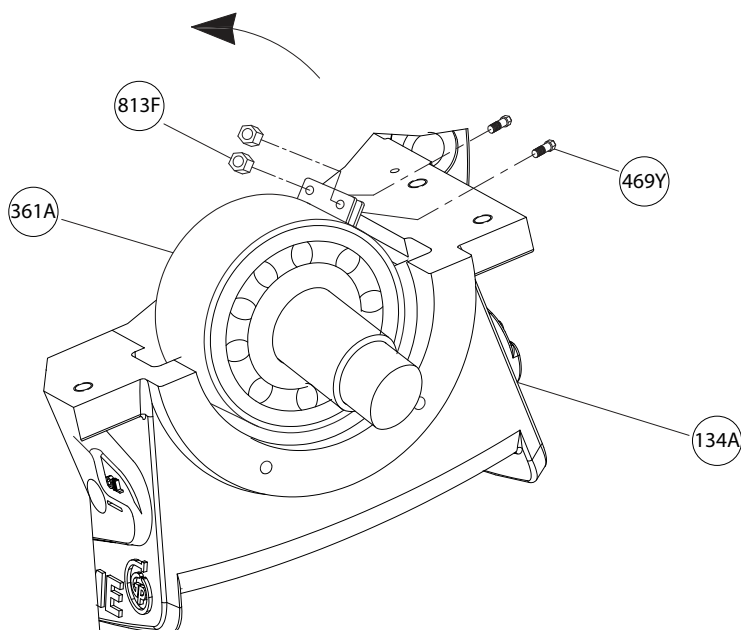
Demontaż łożyska ślizgowego i wzdłużnego
